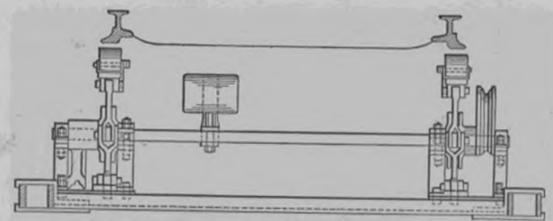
COUPE EN TRAVERS (POUR TRAMWAY ÉLECTRIQUE)
